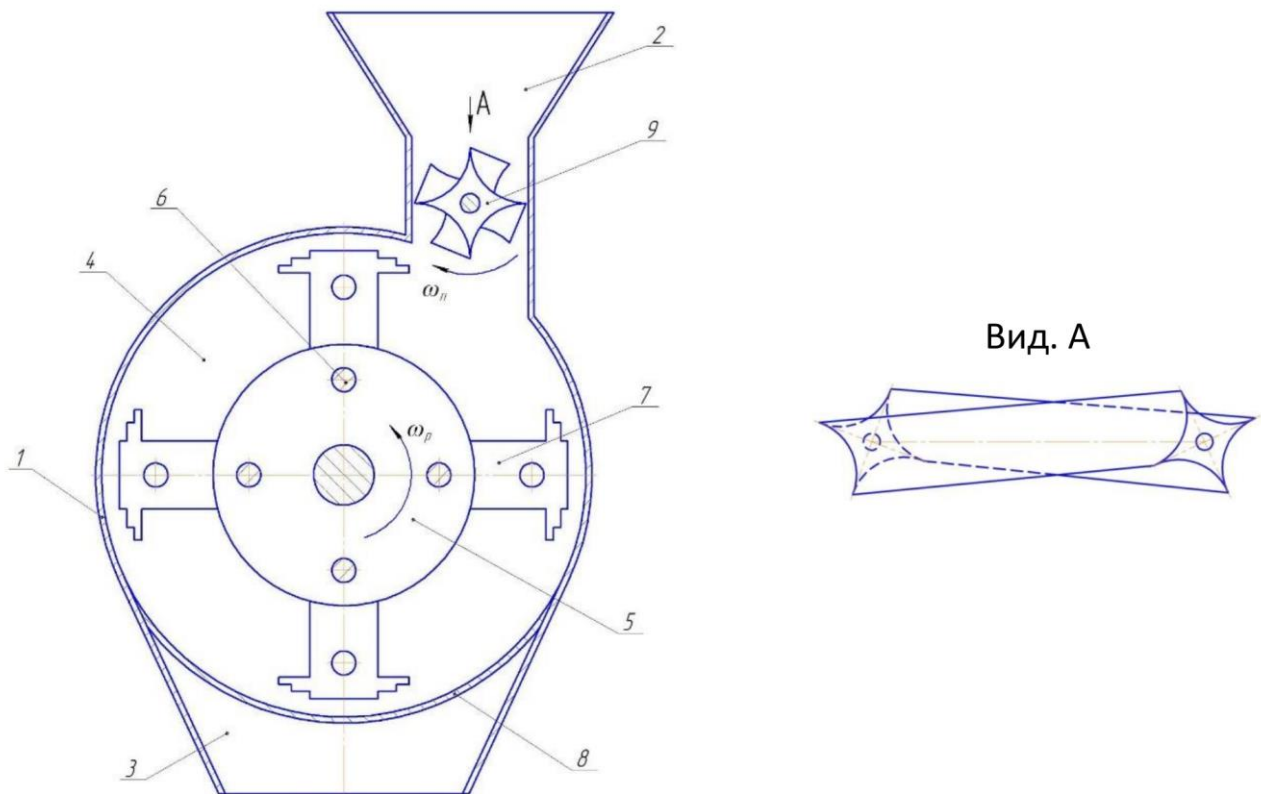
Молоткова дробарка: 1 – циліндричний корпус; 2 – завантажувальний бункер; 3 – вивантажувальне вікно; 4 – дробильна камера; 5 – ротор; 6 – палець; 7 – молоток; 8 – решето; 9 – живильний пристрій [3].
